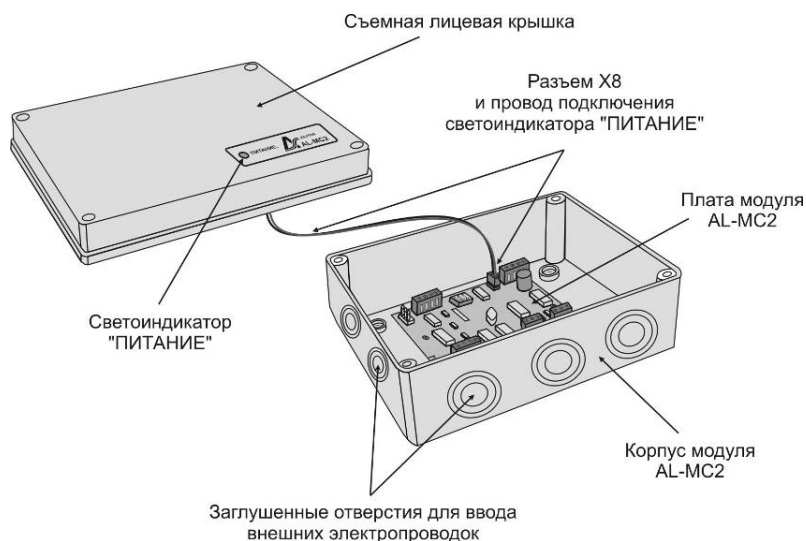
Общий вид модуля AL-MC2 (лицевая часть корпуса снята)
